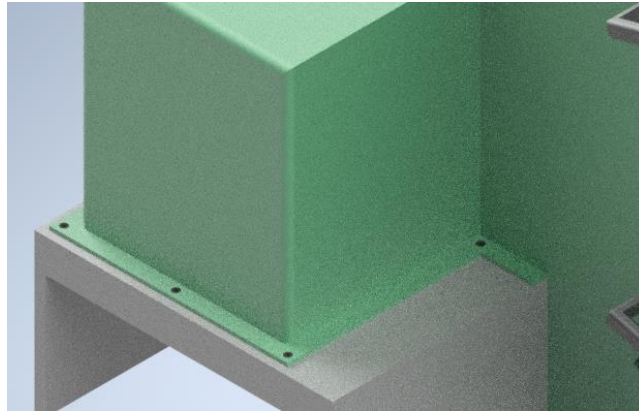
Anclaje tapa del motor y ejes motrices (2)
